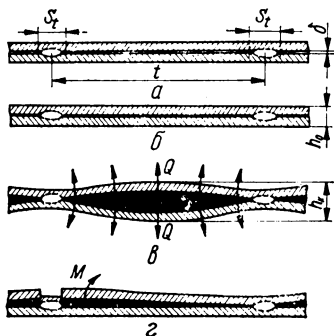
Механизм коррозионного разрушения деталей, соединенных контактной сваркой:
